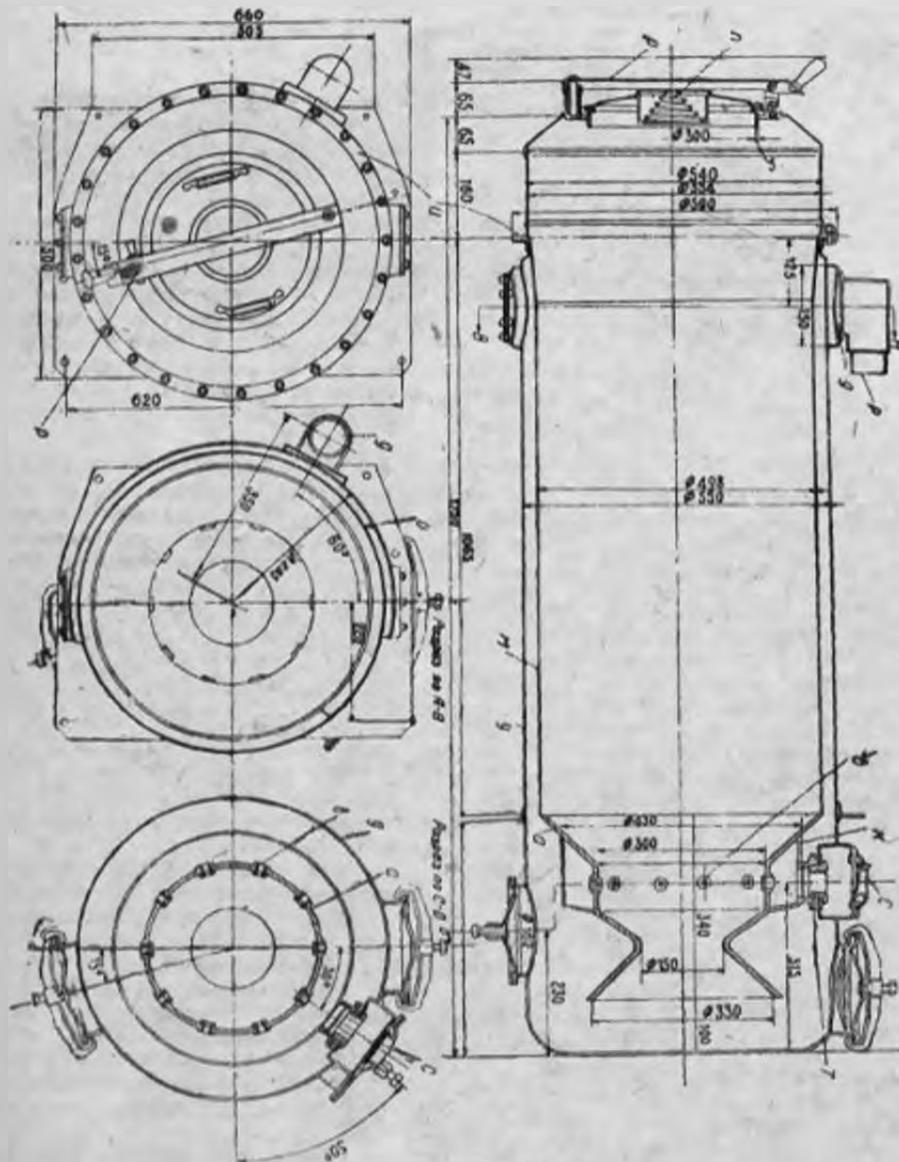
Газогенератор, установленный на машине ЗИС: м—внутренний кожух, у—наружный кожух, в—топливник, л—сопла, к—воздушная коробка, п—пружина, д—патрубок отбора газа, с—возвратный клапан
